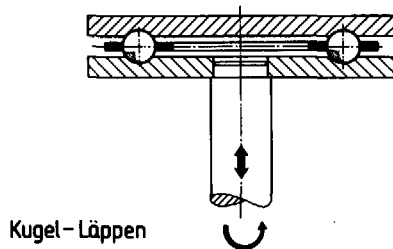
Prinzipskizze einer Kugel-Läppmaschine
